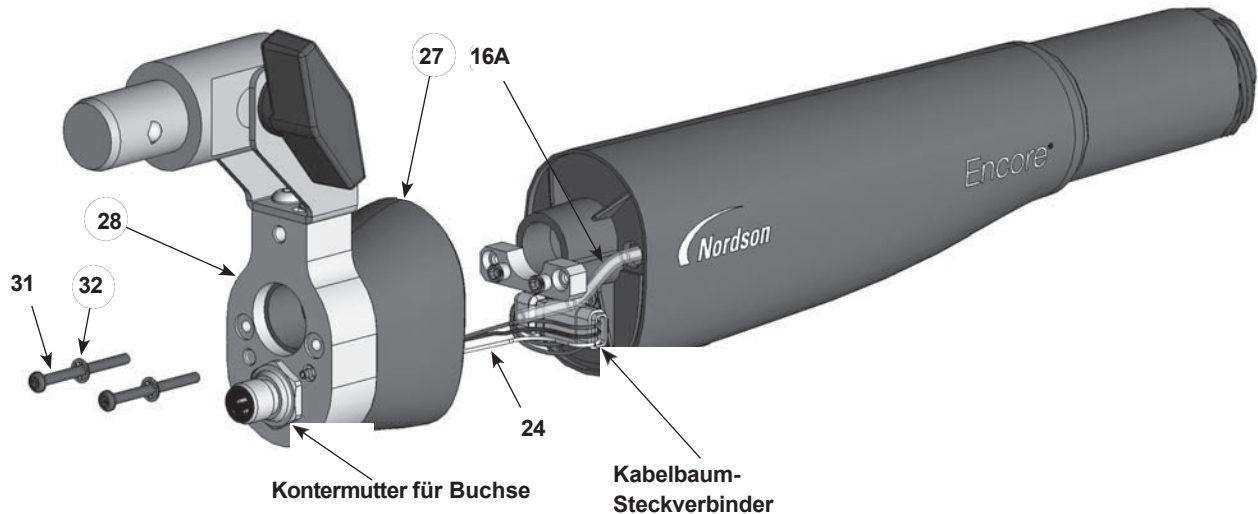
Demontage der Pistole – Austausch des Pulverrohrs
